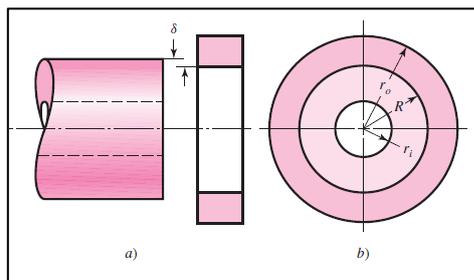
a) Partes no ensambladas; b) Partes ensambladas (SHIGLEY-2008, PÁG 69 CAP 3).
